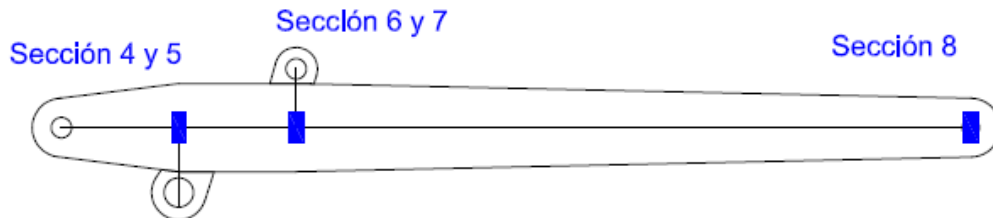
Secciones sobre las que se han medido esfuerzos en pluma 2
